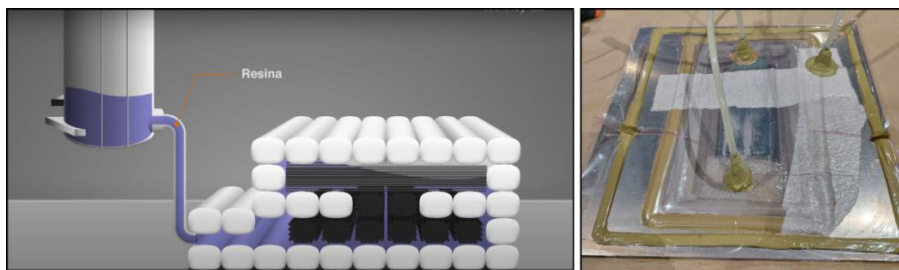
Esquema conceptual y montaje experimental de un proceso de fabricación de moldeo por resina líquida de una preforma.
